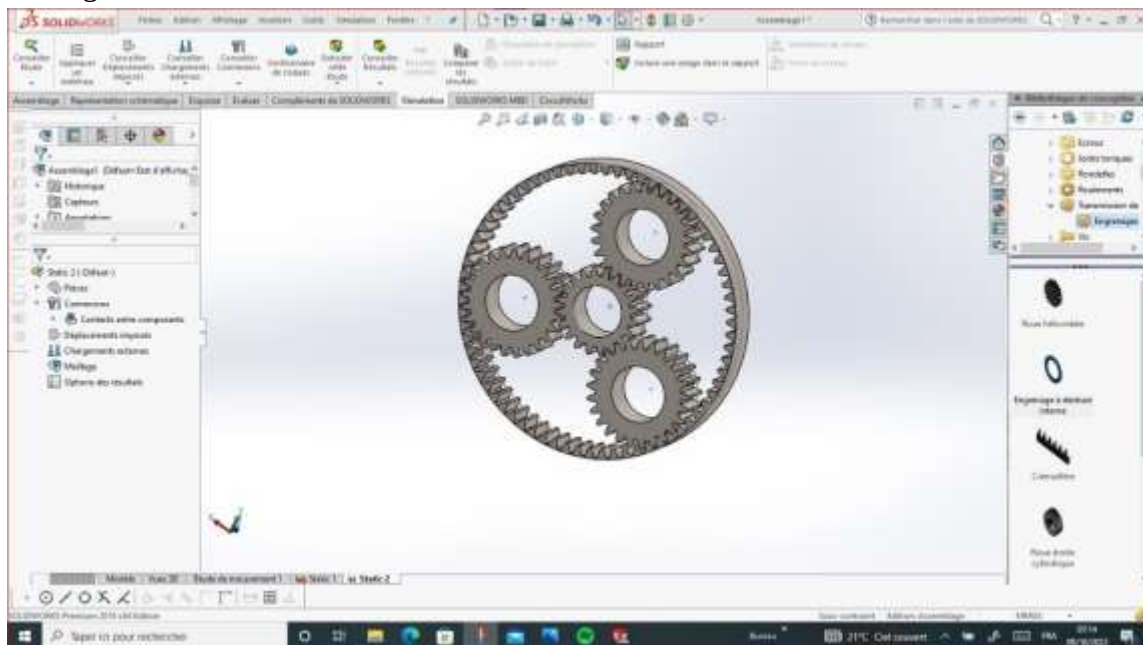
Assemblage d'engrenage de réducteur (Solidworks).
